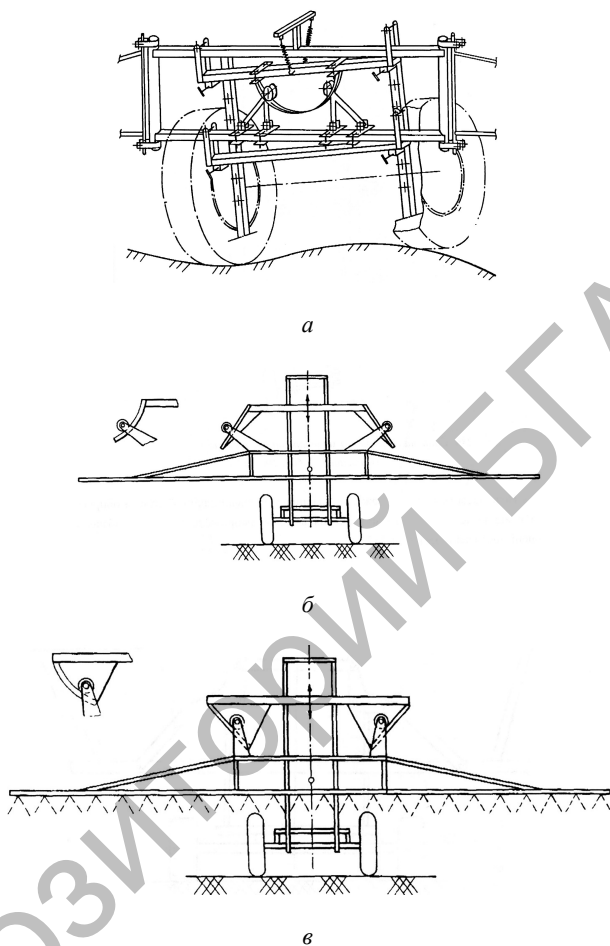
Подвески штанг опрыскивателей с криволинейной опорной поверхностью [38]
